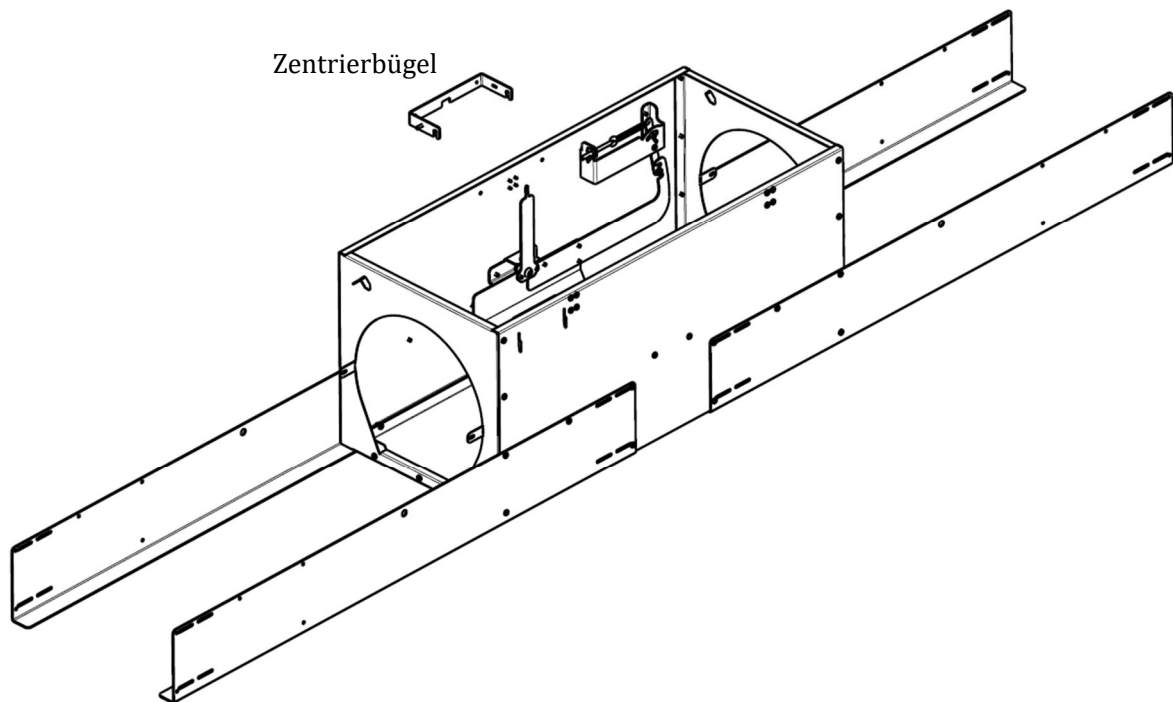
Hauptkasten mit Grundrahmen und demontiertem Zentrierbügel
